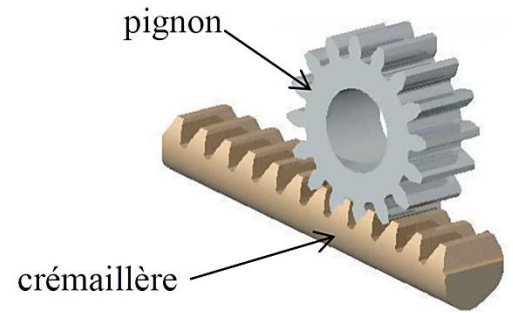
transformation de mouvement par engrenage pignon-crémaillère
